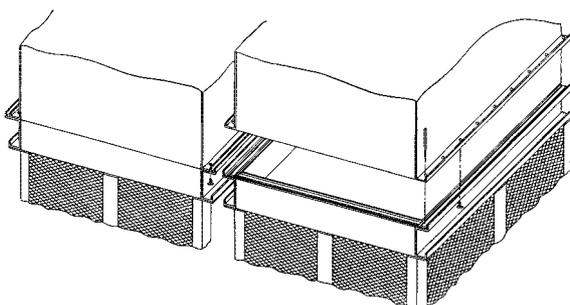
Verschrauben des Oberteils mit dem Unterteil
